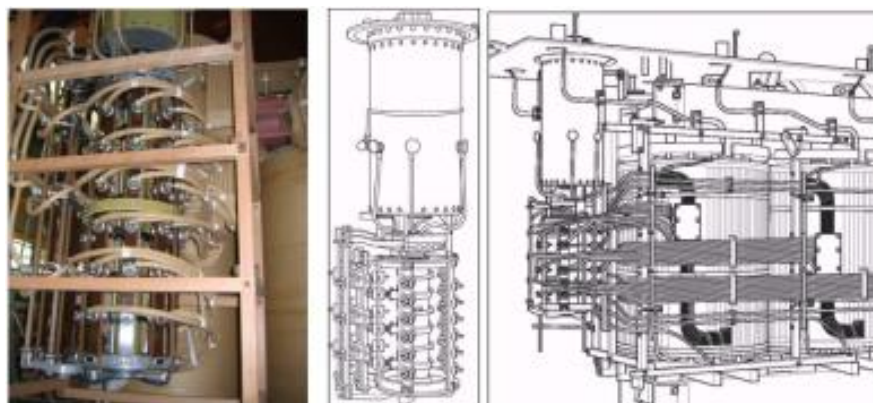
РПН печного трансформатора: а – общий вид; б – устройство; в – расположение и соединения внутри основного бака
